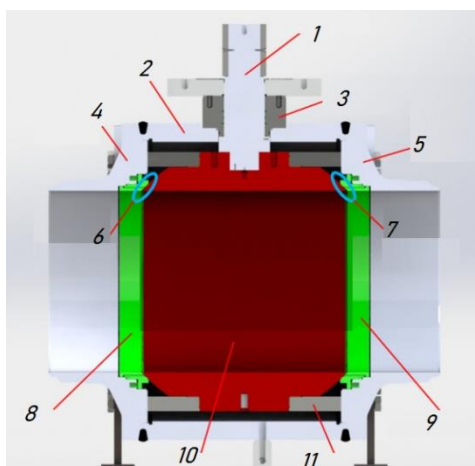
Компоненты шарового крана: 1 – рабочий стержень; 2 – основной корпус; 3 – соединительный узел; 4 – вторичный корпус выше по потоку; 5 – вторичный корпус ниже по потоку; 6 – верхняя зона уплотнения; 7 – нижняя зона уплотнения; 8 – седло выше по потоку; 9 – седло ниже по потоку; 10 – шар; 11 – направляющая пластина.
